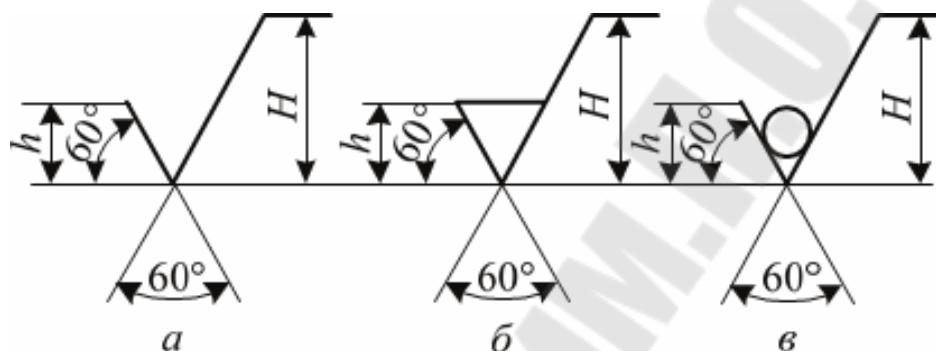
Знаки для обозначения шероховатости на чертежах
